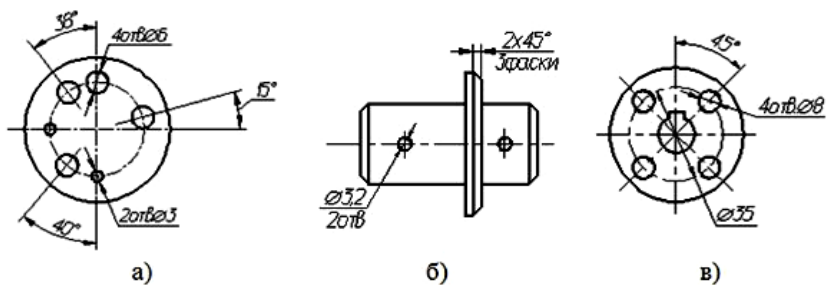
Примеры нанесения размеров одинаковых отверстий
